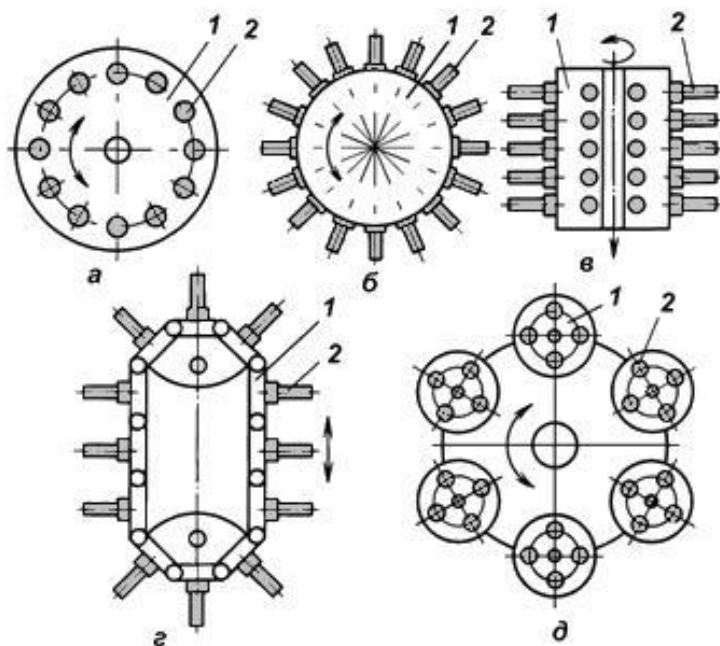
Магазини інструментів верстатів із ЧПК:
